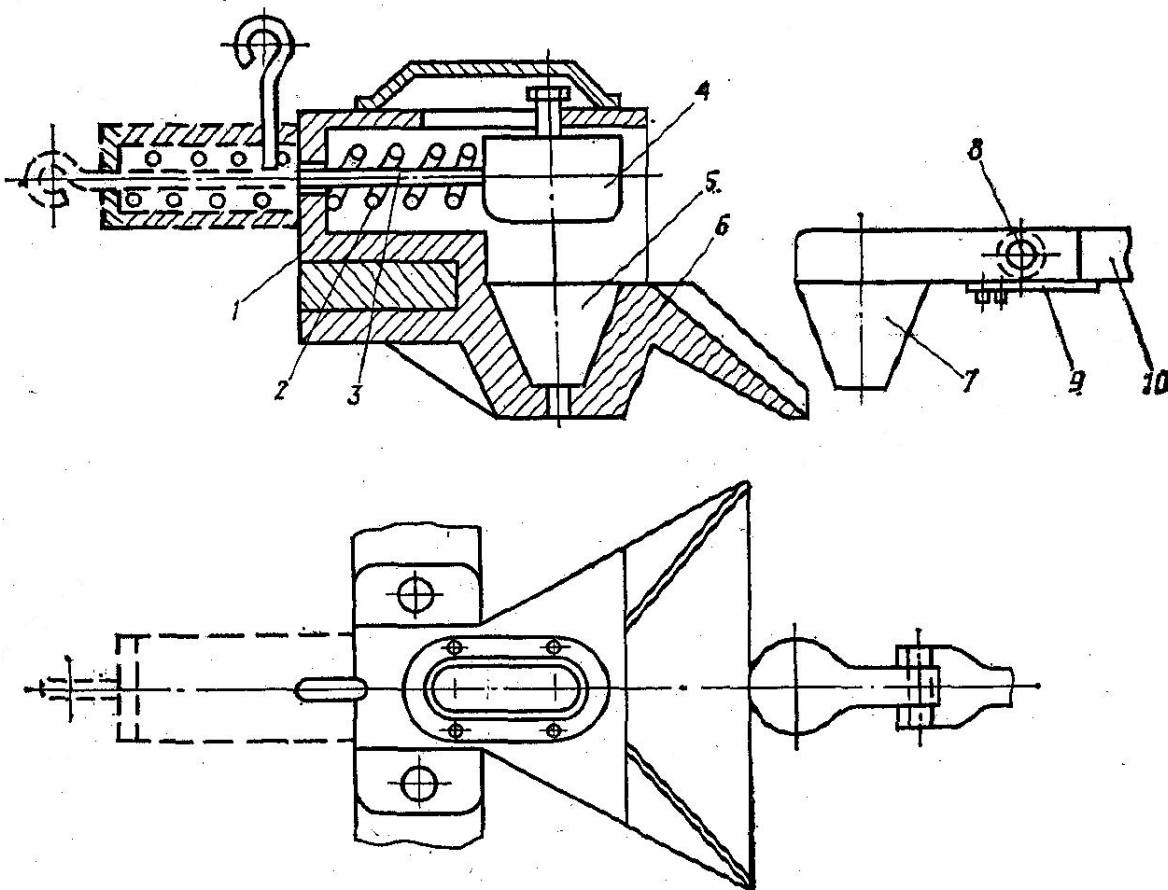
Розріз конструкції автоматичного тягово-причіпного пристрою для тракторів класу понад 3: 1 – корпус; 2 – пружина; 3 – вісь; 4 – упор; 5 – заглиблення; 6 – спрямівник; 7 – виступ; 8 – шарнір; 9 – пластинчаста пружина; 10 – сниця
